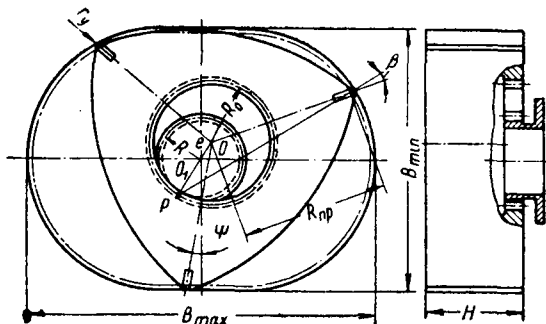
Кинематическая схема роторно-поршневого двигателя с планетарным движением ротора
